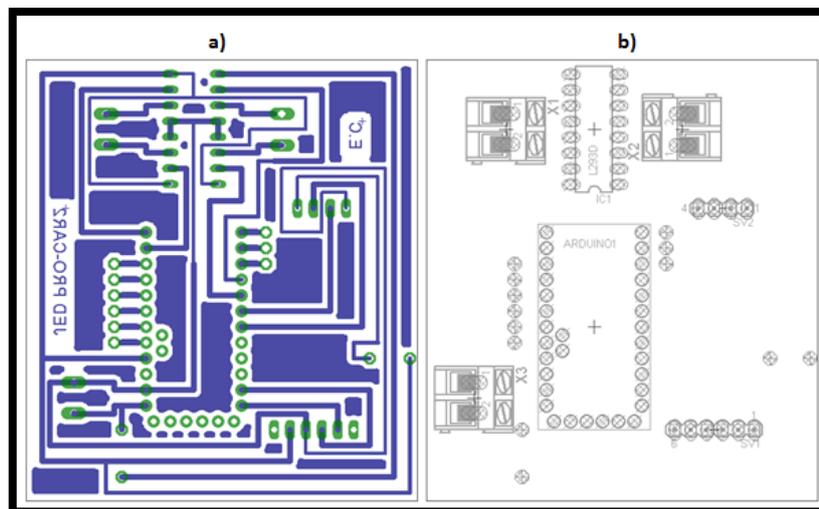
a) Vista Posterior de la placa b) Ubicación de elementos
